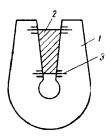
Шаблон для проверки профиля коллекторных пластин;
